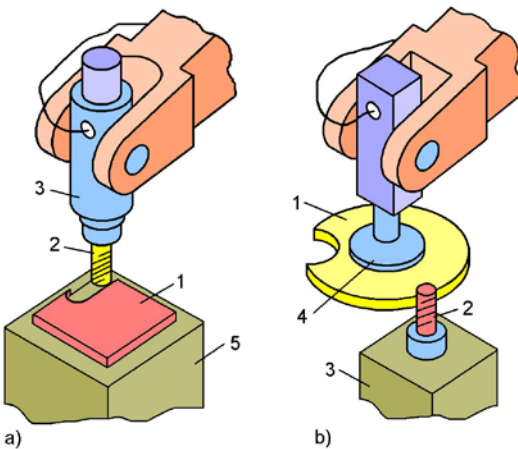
Einsatz von Industrierobotern als Bearbeitungsmaschine.
